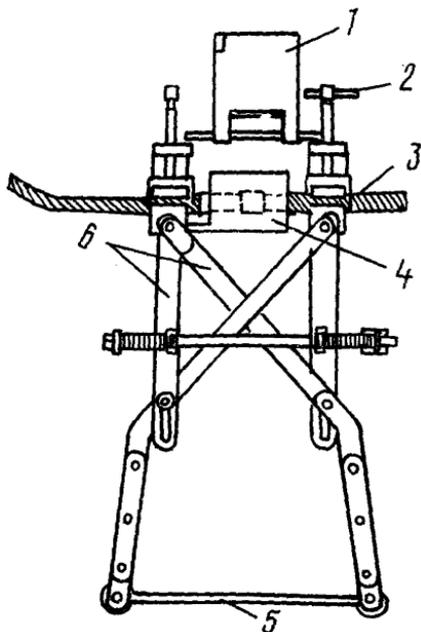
Сварочные клещи типа АТСП-50-185:
